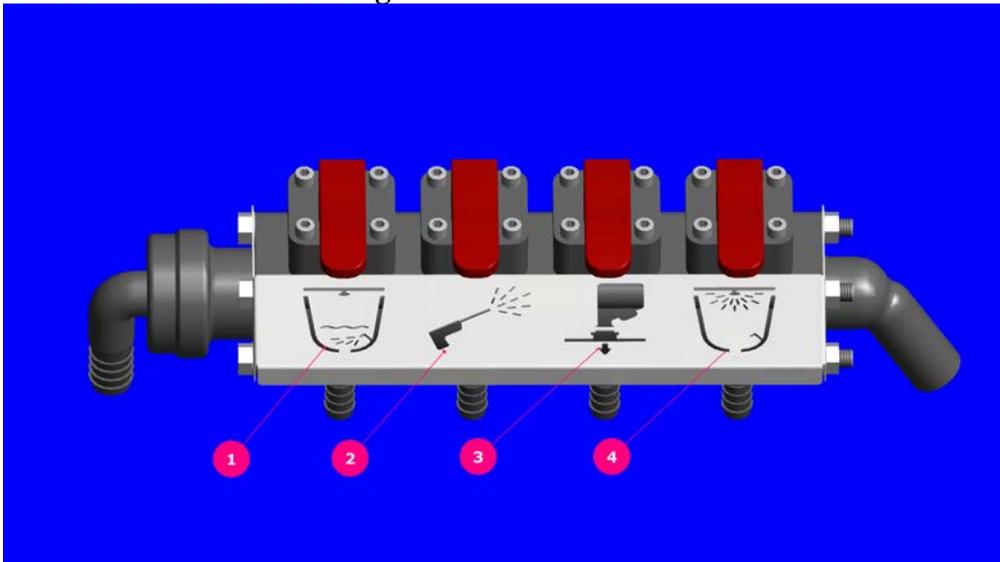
/2 Beschreibung der Steuerhebel der Einspülschleuse
